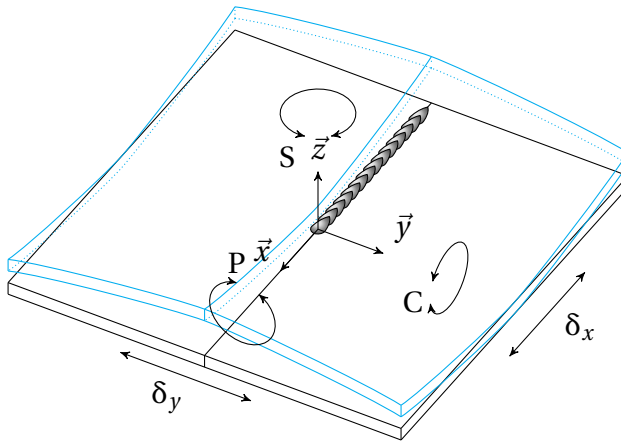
Déformations typiques de soudage.
